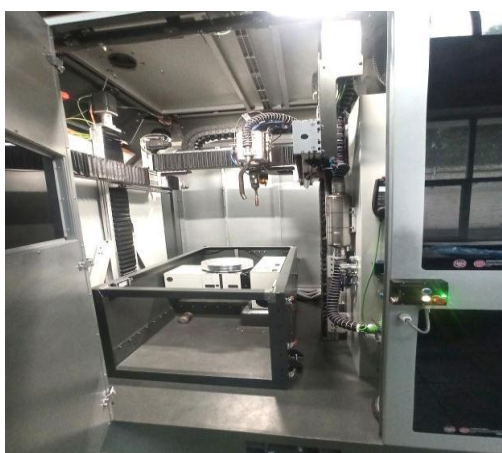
Рабочая камера портальной установки для осуществления электродуговой наплавки (WAAM)
